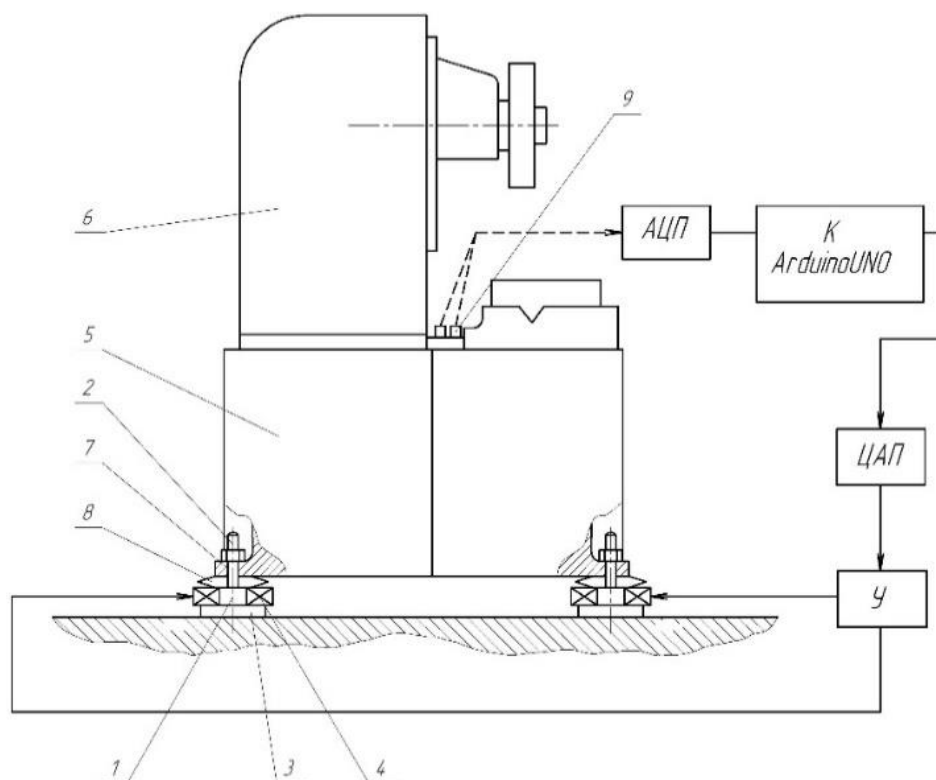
Схема опоры металлорежущего станка с активной виброизоляцией
